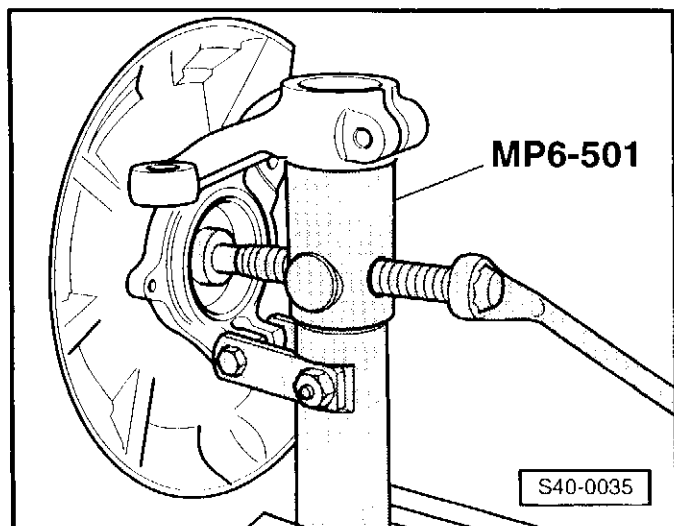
Выпрессовка ведущего диска ступицы колеса из крышки подшипника ступицы колеса
